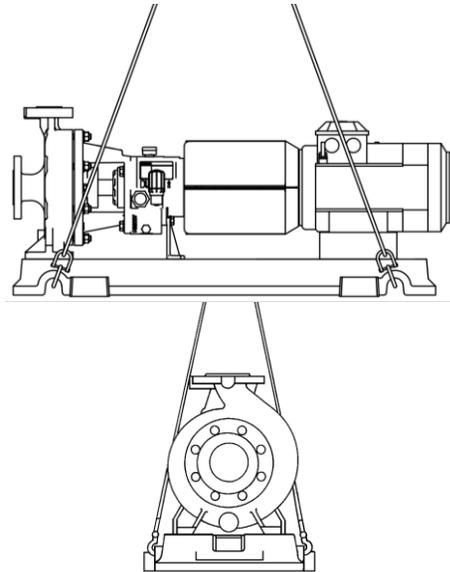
Levage pomp sur châssis fonte ou mécano-soudé
